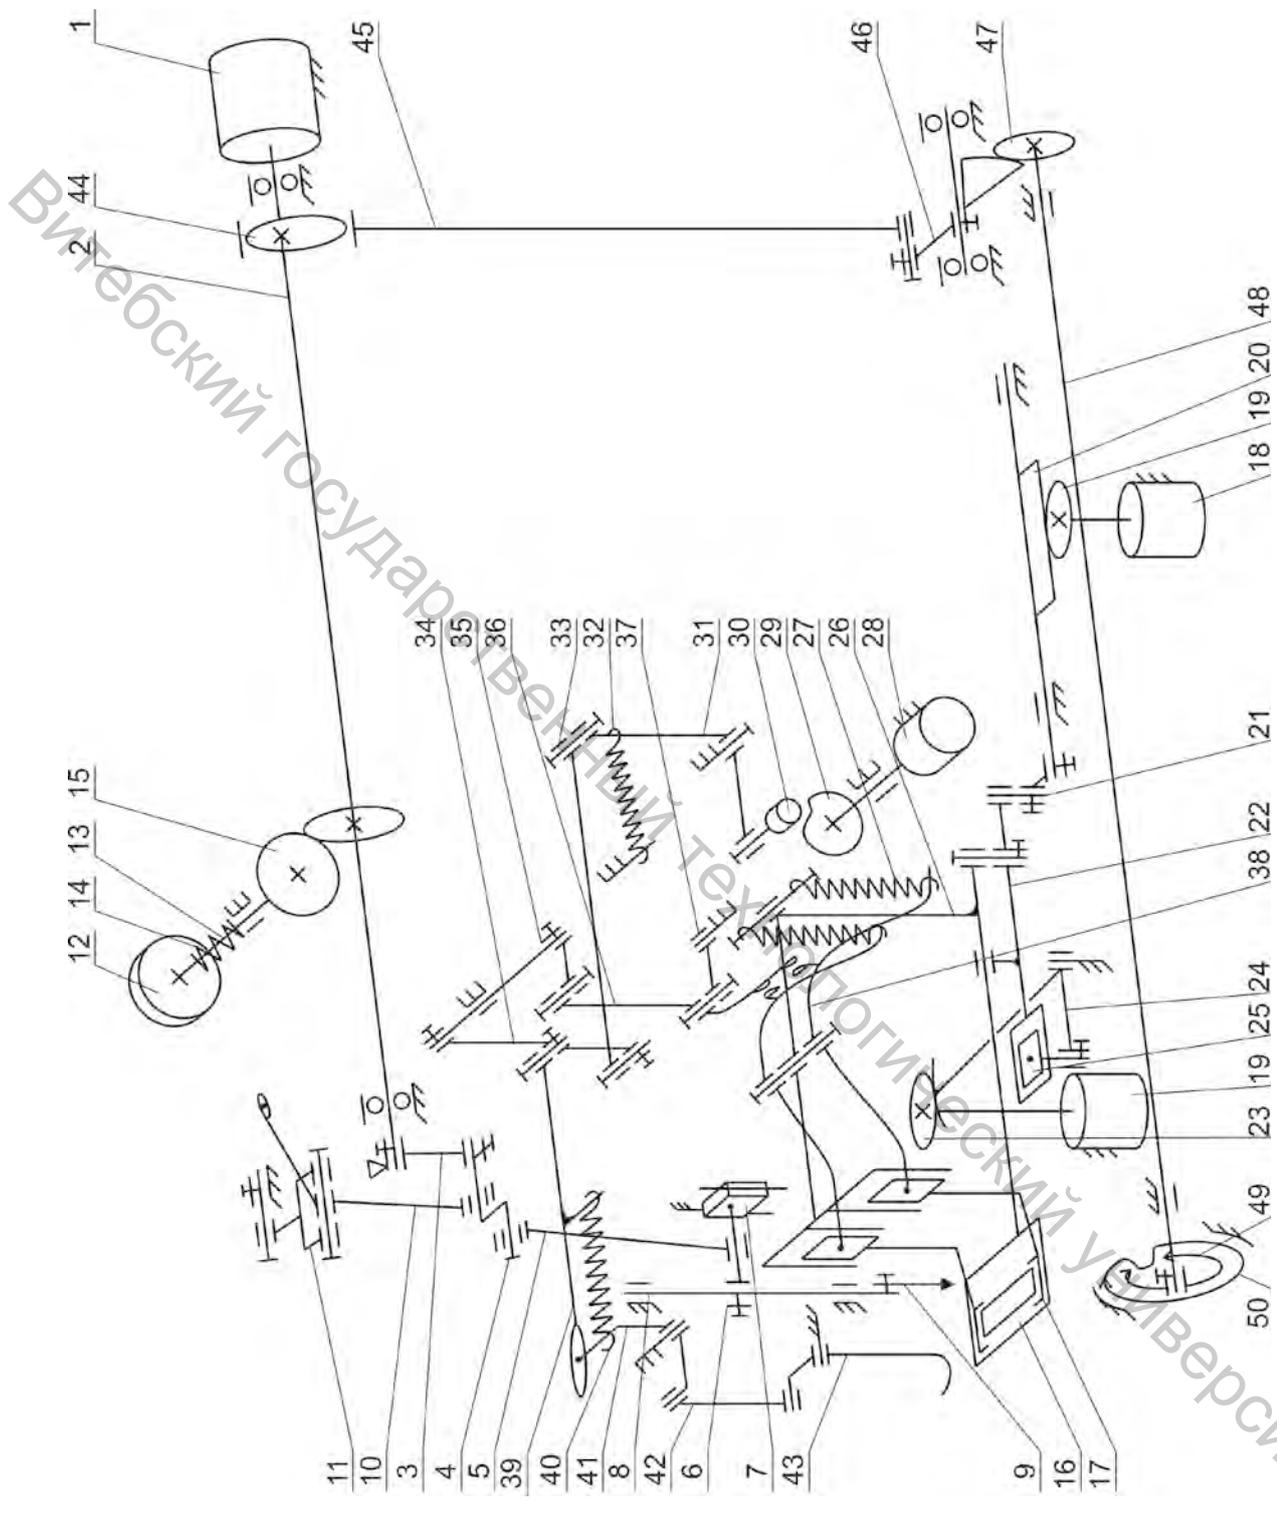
Кинематическая схема полуавтомата LK-1900B Juki
